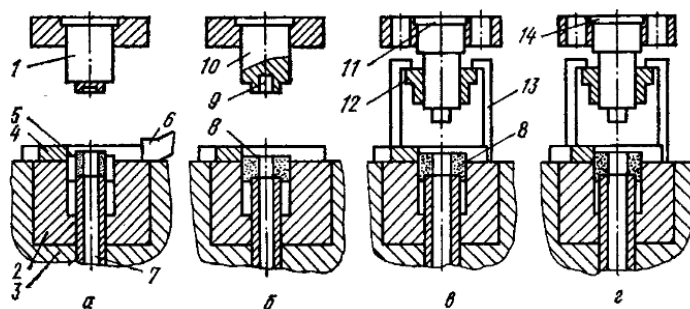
Конструктивні схеми штампів, що використовуються для ГШ [36]
